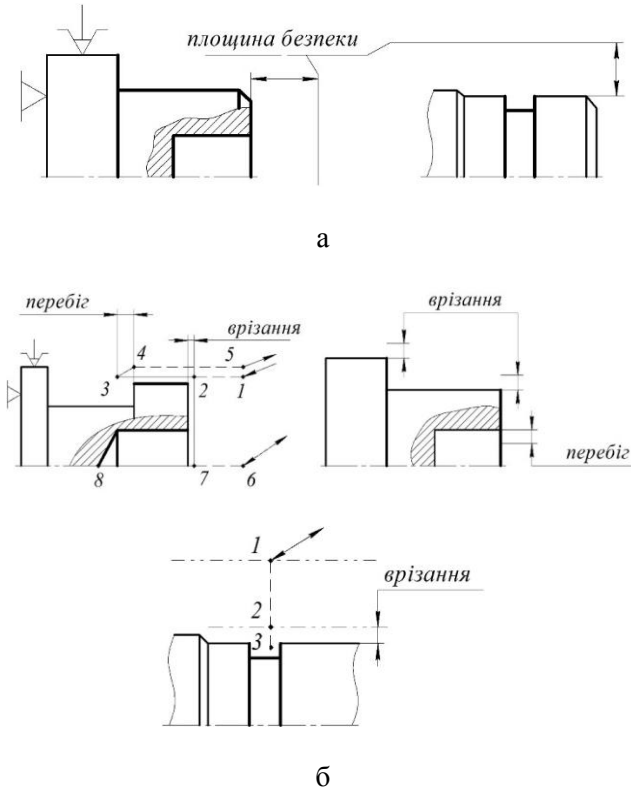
Типові схеми зняття припусків для різних поверхонь
